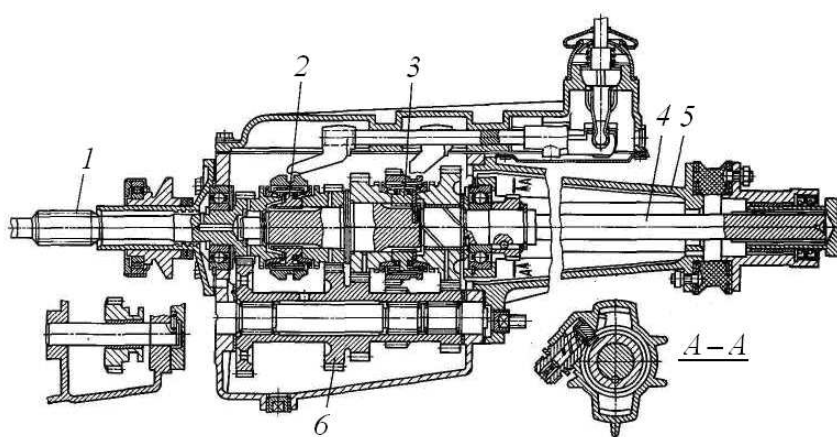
Трехвальная коробка передач автомобиля ГАЗ-3102 [37]: 1 – ведущий вал; 2 – синхронизатор третьей и четвертой передач; 3 – синхронизатор первой и второй передач; 4 – ведомый вал; 5 – удлинитель; 6 – блок зубчатых колес промежуточного вала
